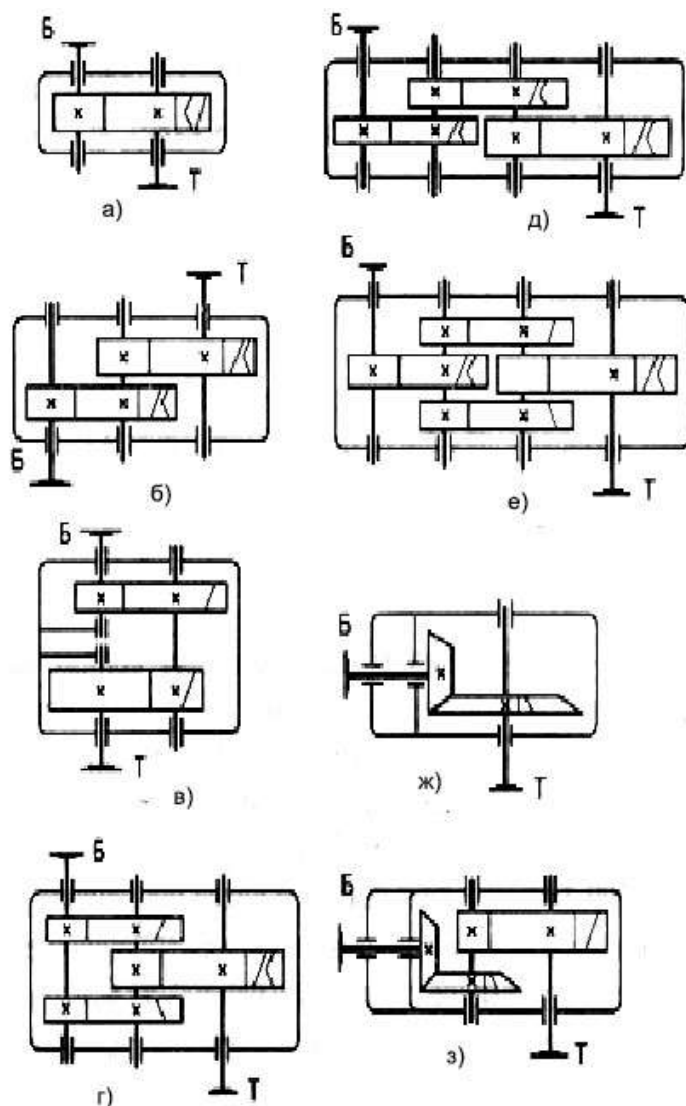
Наиболее распространенные схемы зубчатых редукторов: а — одноступенчатый; б — двухступенчатый развернутый; в — двухступенчатый соосный; г — двухступенчатый с раздвоенной ступенью; д — трехступенчатый развернутый; е — трехступенчатый с раздвоенной промежуточной ступенью; ж — конический; з — коническо-цилиндрический
